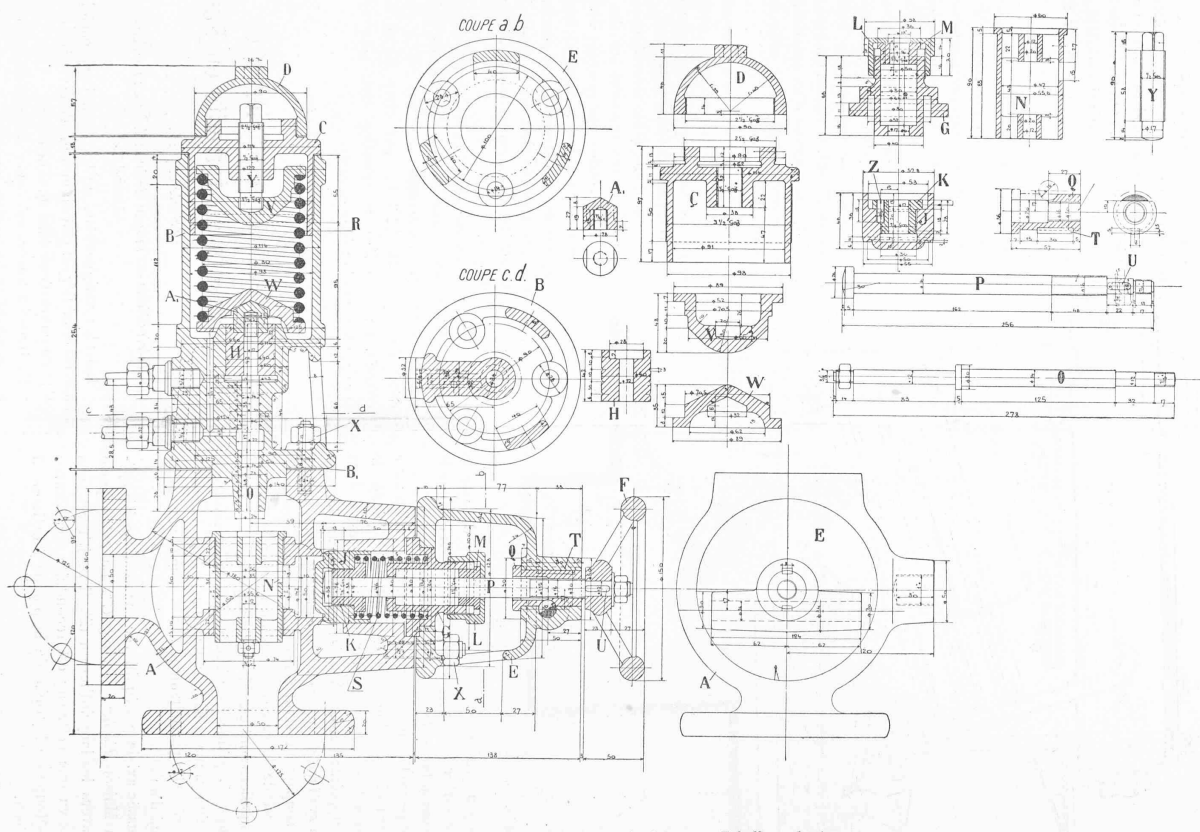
Détail de la soupape du régulateur. — Echelle — 1 : 4.
